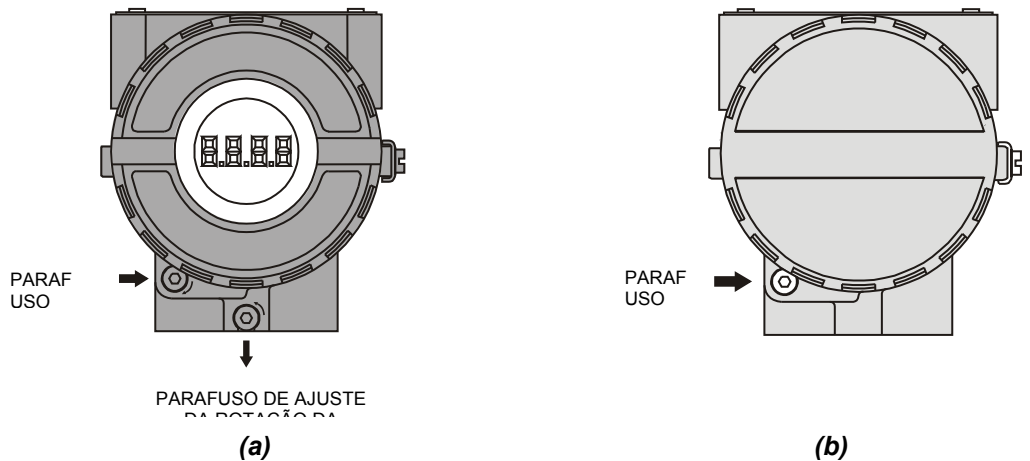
Trava da Tampa e Parafuso de Ajuste da Rotação da Carcaça (a) Lado da Placa Eletrônica (b) Lado do Terminal de Conexões
